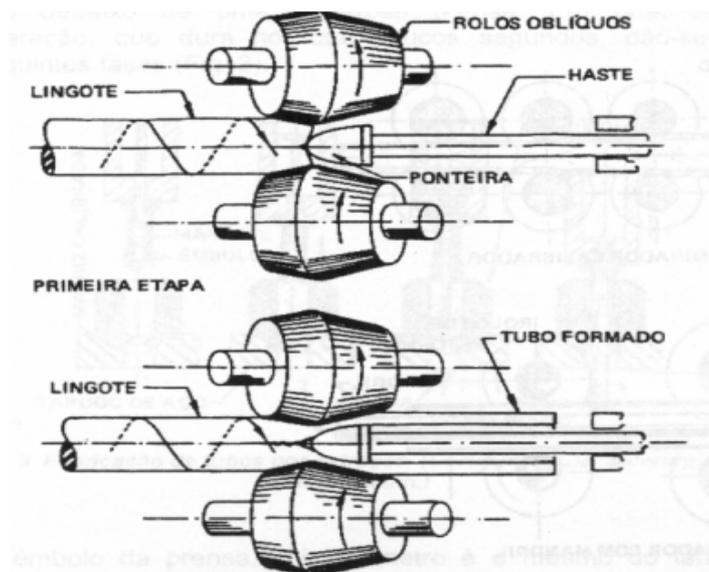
Fabricação de tubos pelo Laminador oblíquo "Mannesmann".
